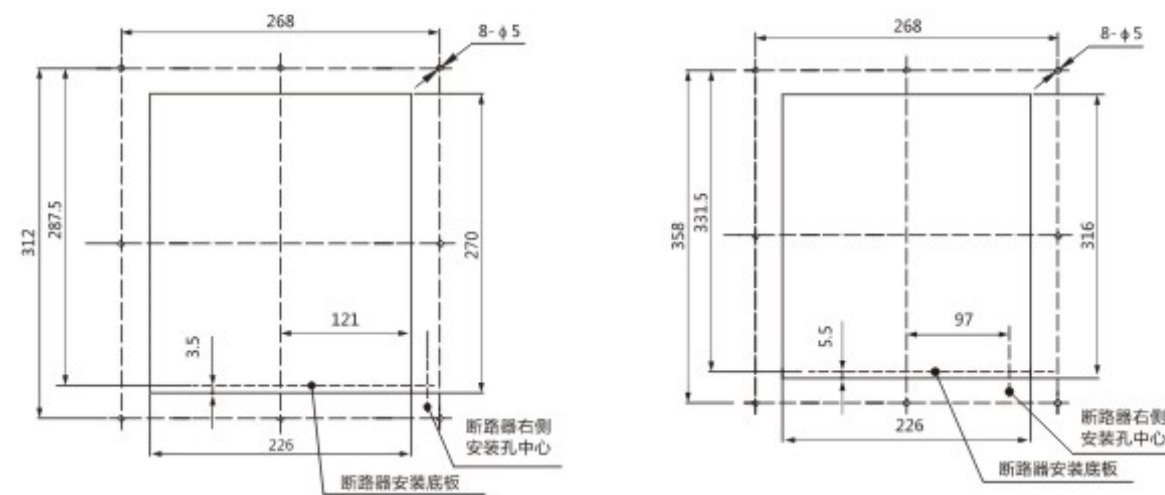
FSW50-200A~1000A抽屉式断路器 Figure 3: Draw-out type circuit breakers dimensions
